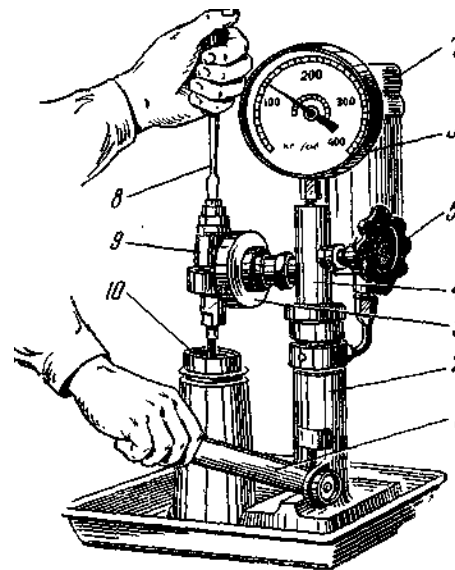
Испытание и регулировка форсунки при помощи прибора КИ-562:
